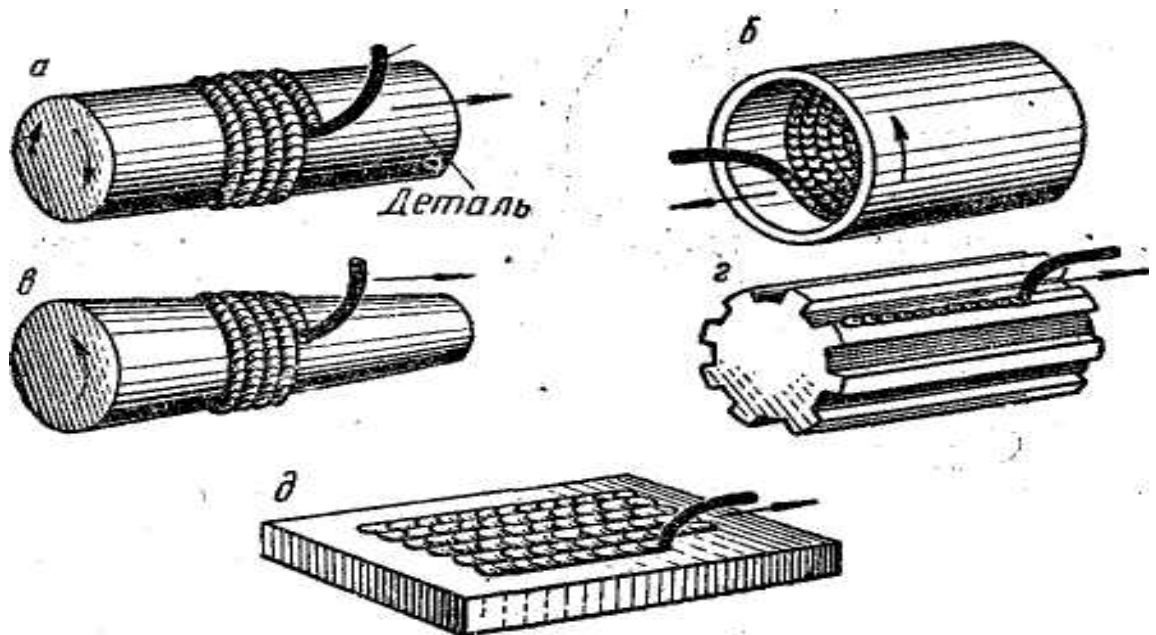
Різні варіанти вібродугового наплавлення: а — наружні циліндричні поверхні; б — внутрішні циліндричні поверхні; в — конічні поверхні; г — бічні поверхні шліців (чи пазів шпонок); д — плоскі поверхні
